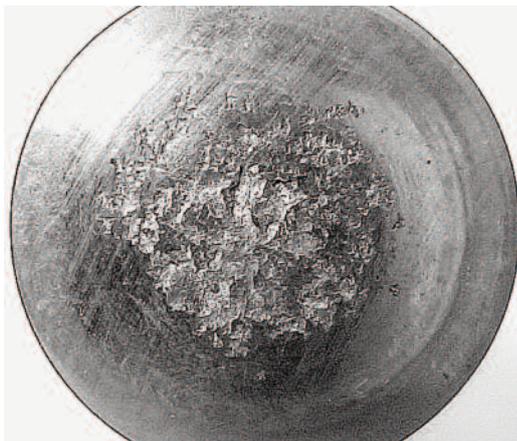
Pitting ocurrido solamente en el centro de la base
